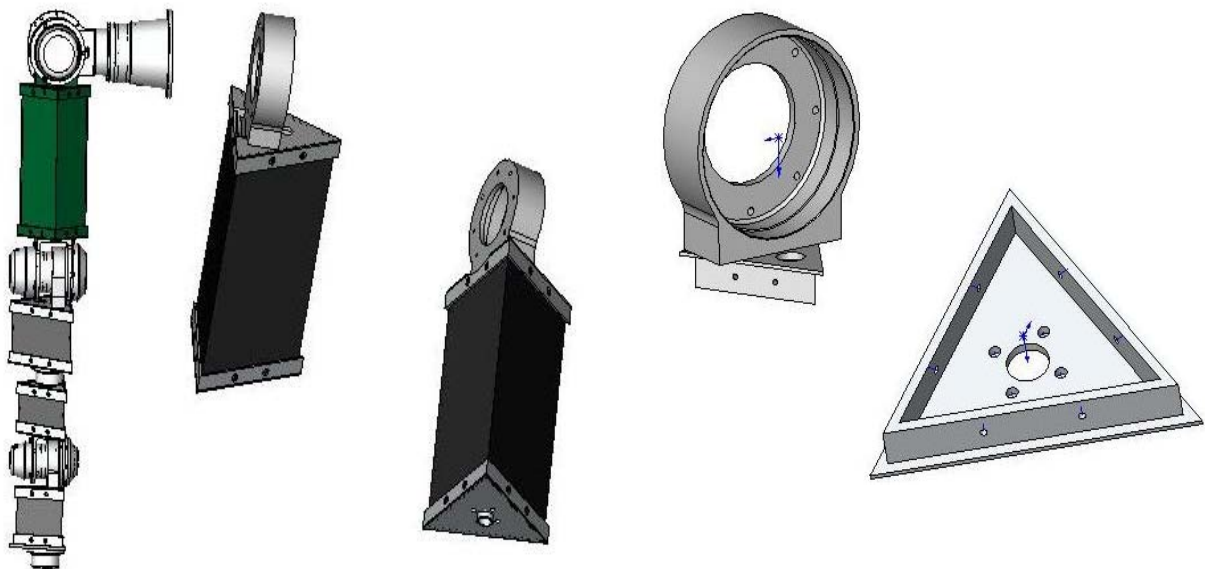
Vista sub-ensamblaje sección triangular y piezas de la misma sección.
